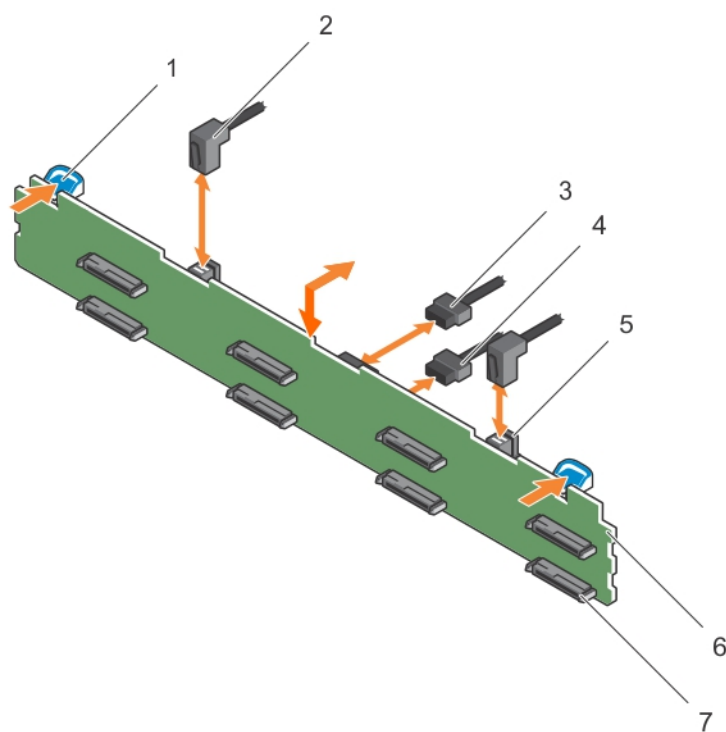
Retrait et installation du fond de panier SAS/SATA (x8) de 3,5 pouces : PowerEdge R730
